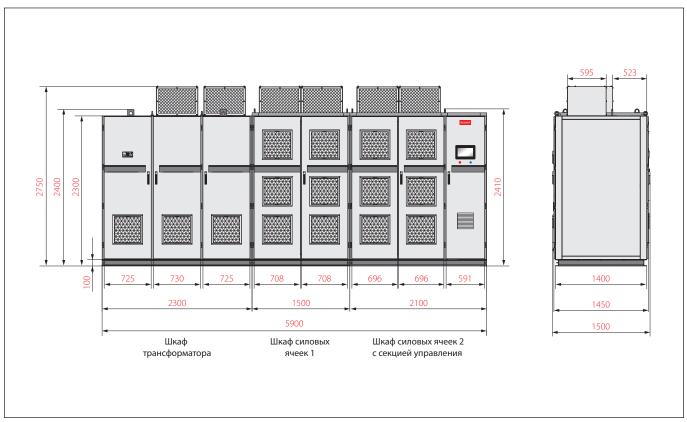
Корпус RA03 на напряжение 6 кВ
